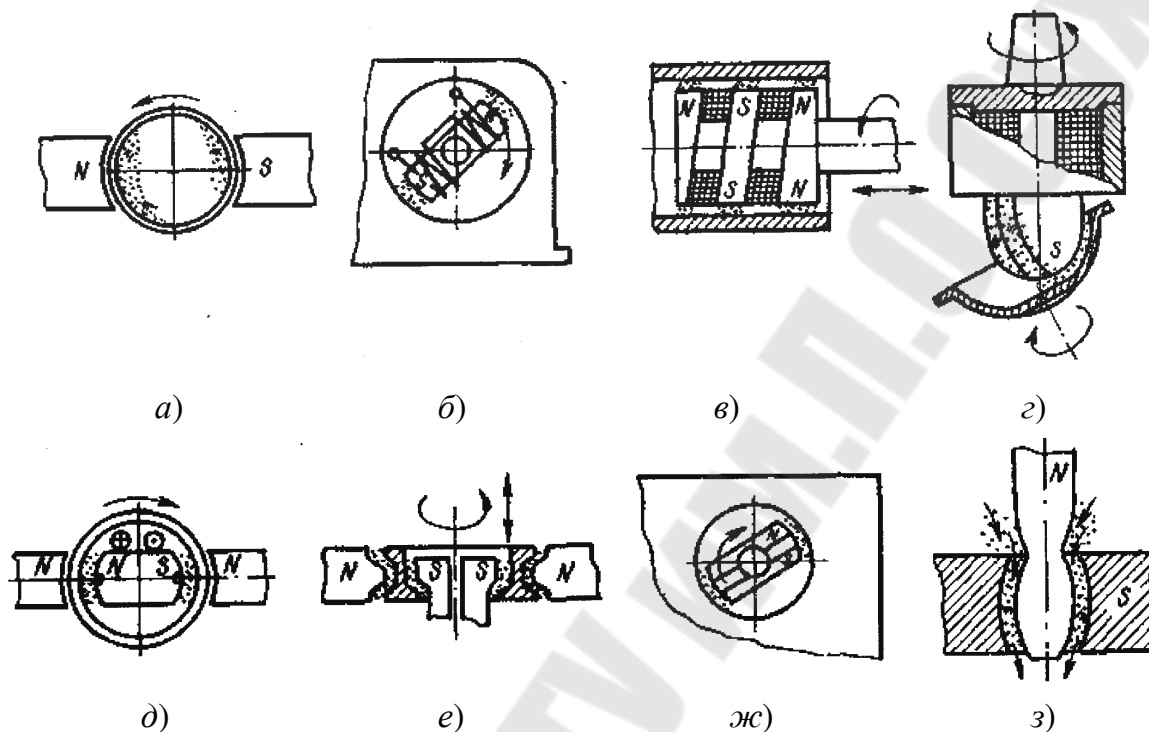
Схемы магнитно-абразивной обработки отверстий
